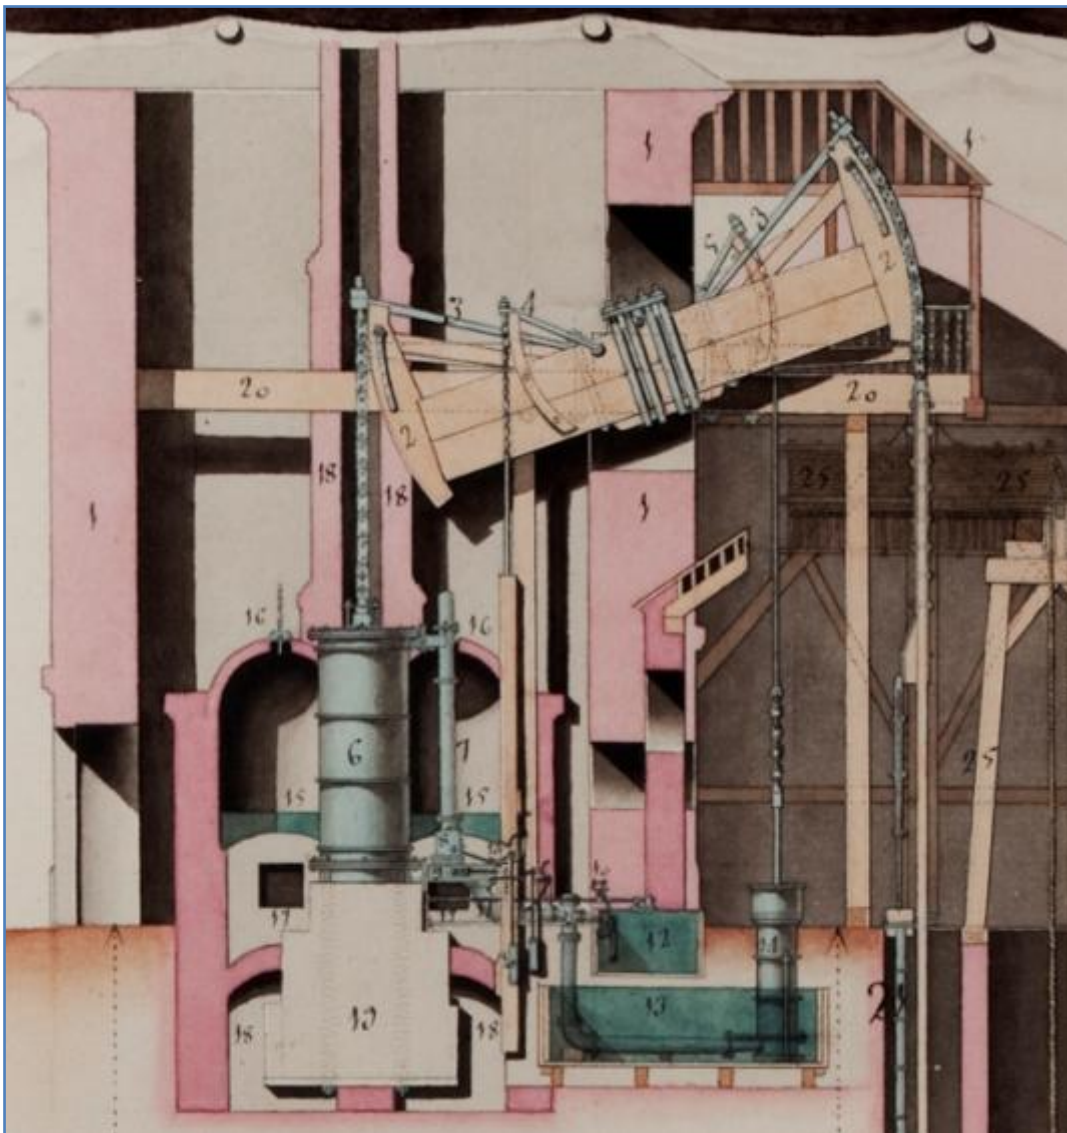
Detalle de la máquina de vapor del plano Nº 12.
